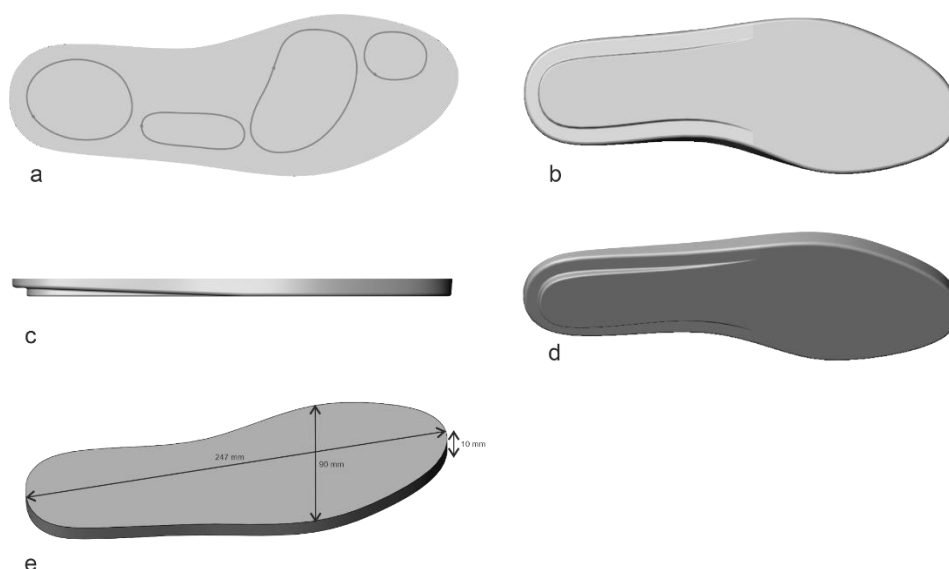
Desenho 3d da entressola, a) vista de cima com identificação das zonas de alívio da pressão plantar, b) vista de baixo, c) vista lateral, d) vista perspetiva de baixo, e) dimensões principais.
